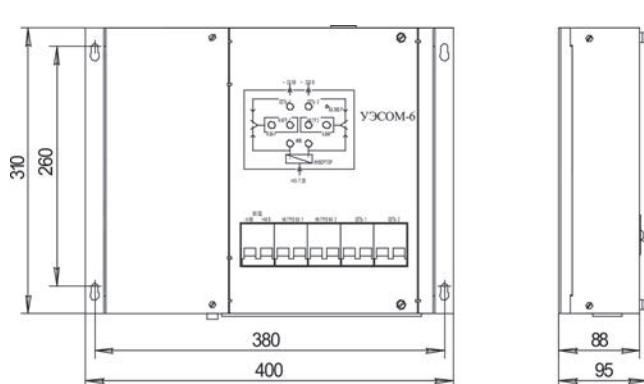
Габаритный чертеж УЭСОМ-6
